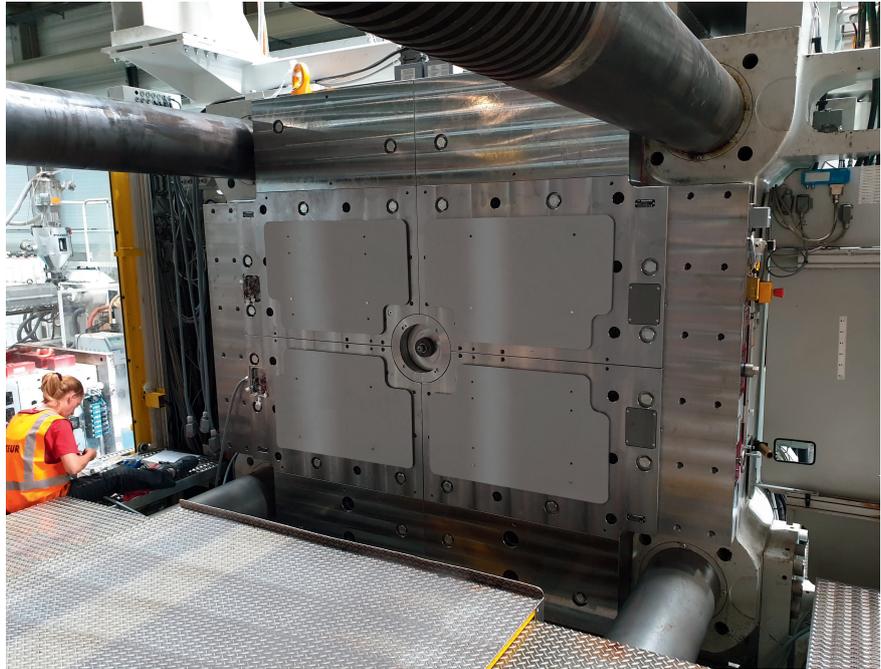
Einbausituation im Werkzeugraum der Engel duo 2700: Magnet-Werkzeugaufspannplatte vor Heißkanal-Adapterplatte. © A&E Produktionstechnik
